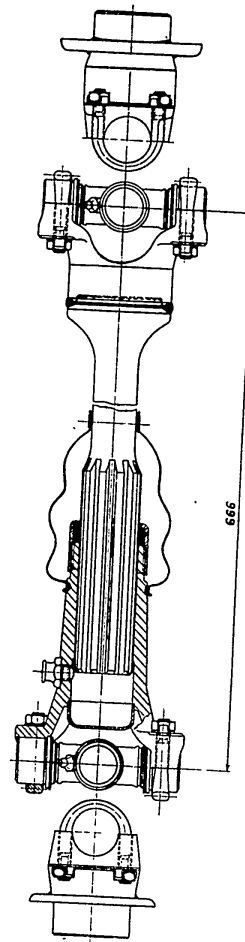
Spojovací hřídel přední nápravy s klouby
